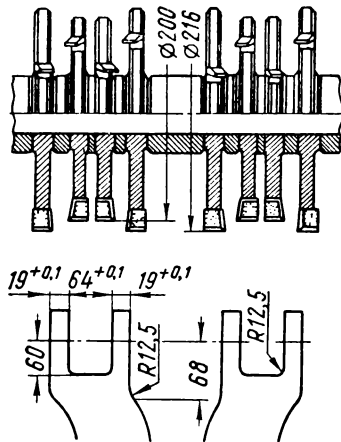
Схема одновременного фрезерования двух деталей с двойной проушиной набором из восьми твердосплавных фрез
